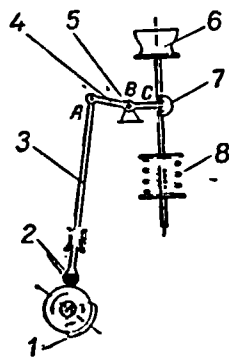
Парораспределительный механизм с кулачной шайбой.
